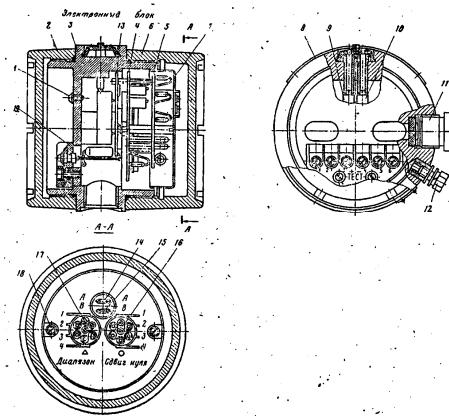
винт для подсоединения экрана кабеля; 2,6 - крышка; 3 - корпус; 4,5,13 - платы; 7 - крышки; 8 -табличка; 9 - корректор настройки «диапазона»; 10 - корректор настройки «нуля»; 11 - кабельный ввод; 12 - винт заземления прибора; 14,15 - перемычки для изменения диапазона измерения; 16 - перемычки для грубой настройки «нуля»; 17 - перемычки для грубой настройки «диапазона»; 18 - винт крепления крышки 7; 19 - клеммная колодка.
